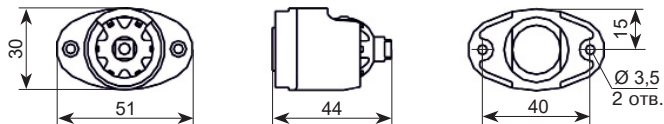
Габаритные и установочные размеры (размеры указаны в мм)
